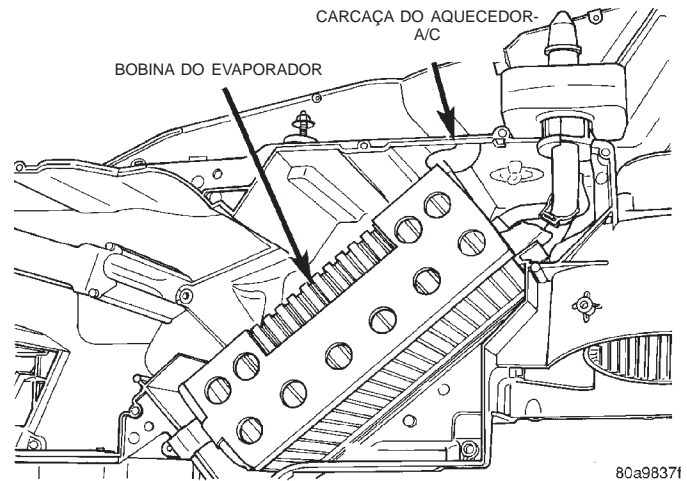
Remoção/Instalação da Bobina do Evaporador
